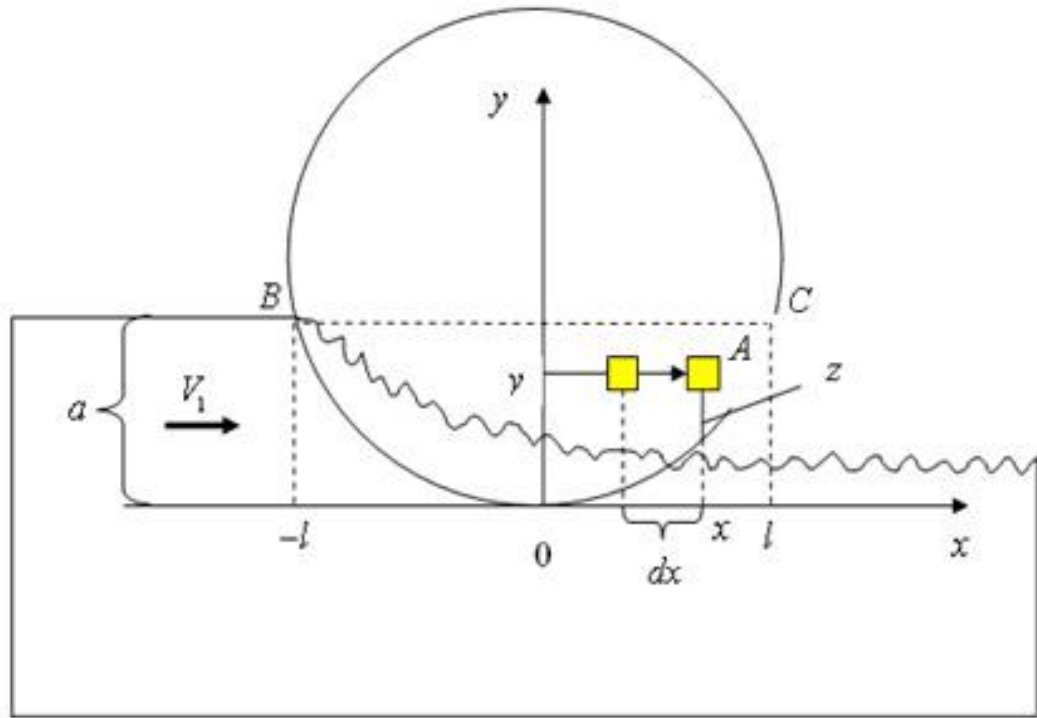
Расчетная схема контакта шлифовального круга с заготовкой
